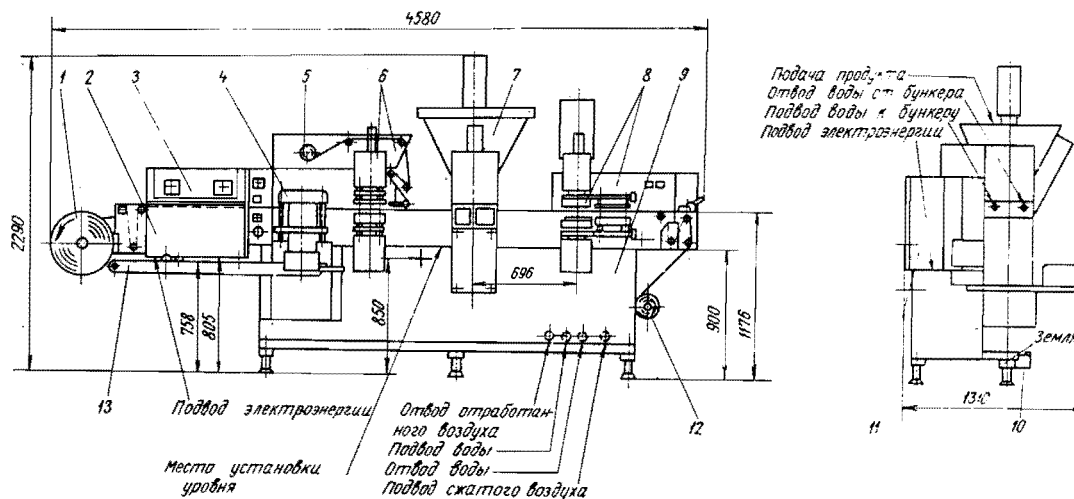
Общий вид автомата фасовочно-упаковочного марки М6-ОРК:
